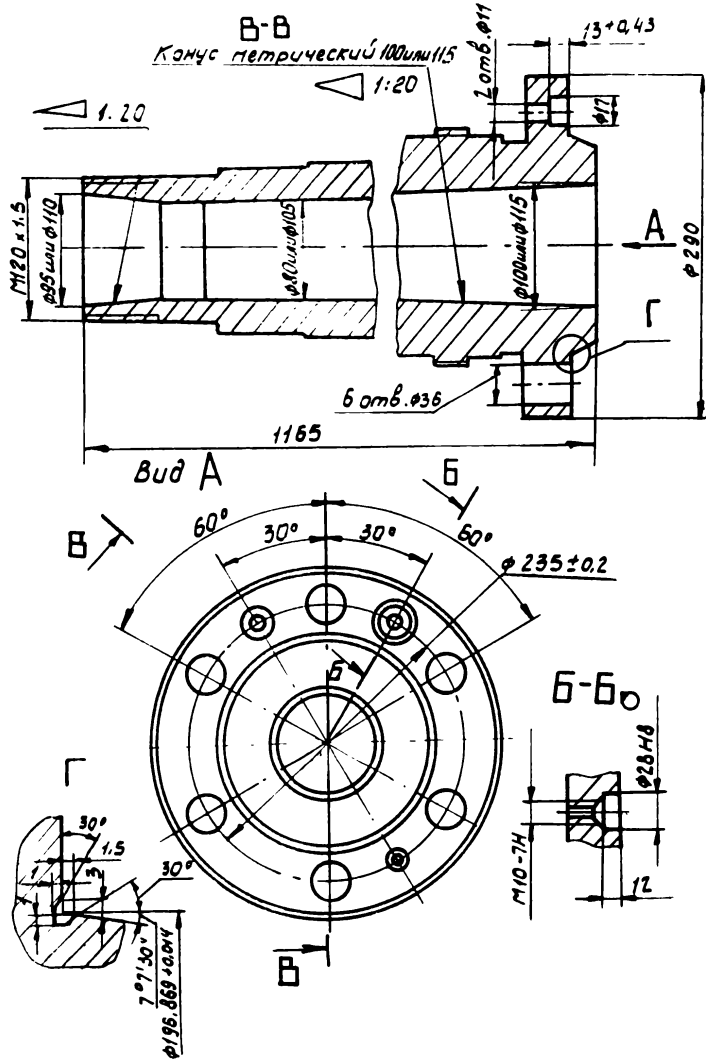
Установка и присоединительные размеры шпинделя бабки передней
